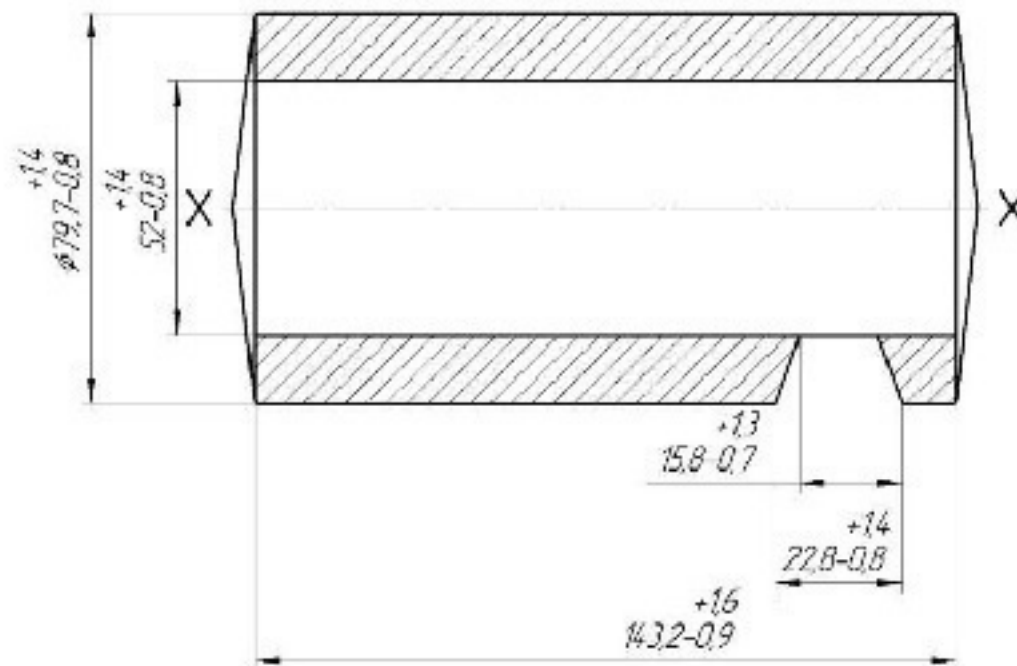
Ескіз заготовки виготовленої на КГШП
